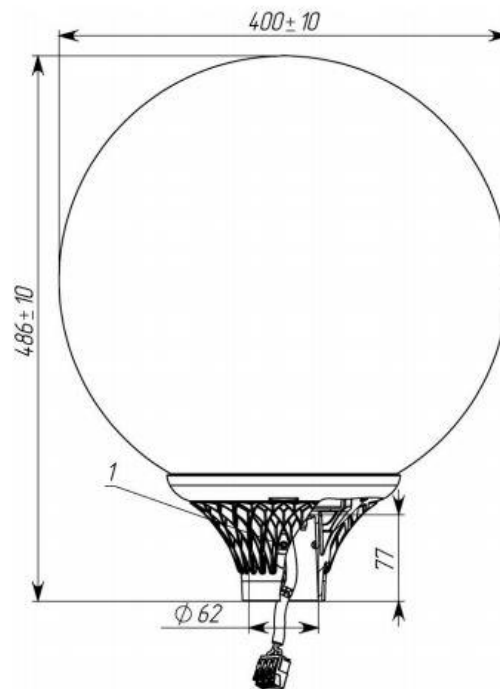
Габаритный вид светильника GALAD Шар LED-40
